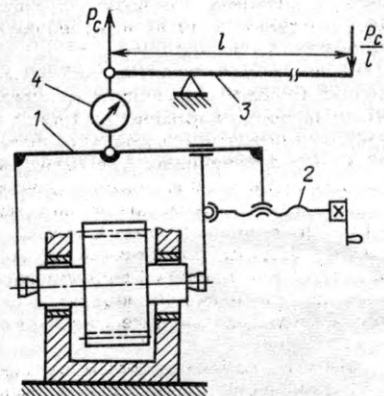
Схема приспособления для установки вала шестерни в положение, соответствующее пуску передачи
